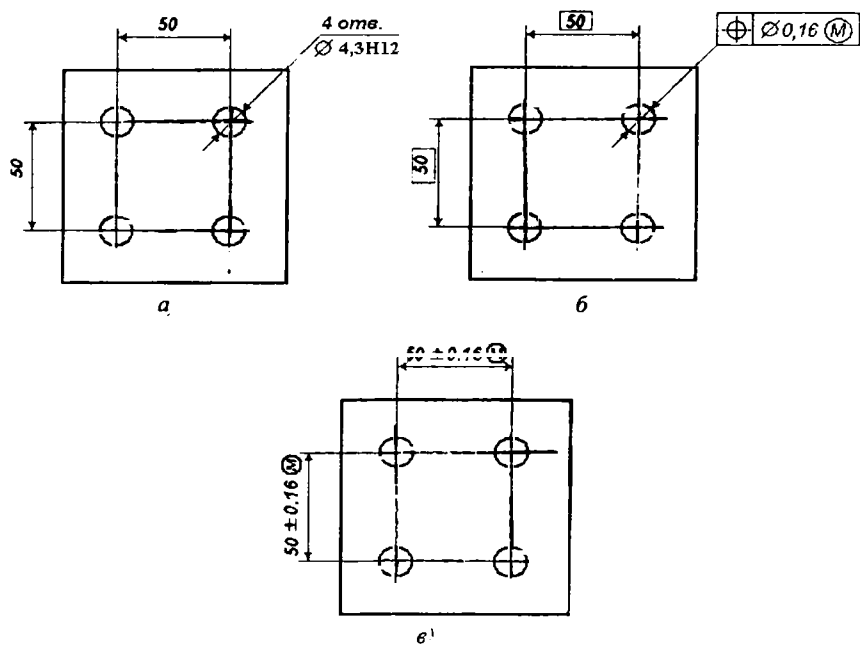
Допуски расположения осей отверстий соединения болтами М4:
